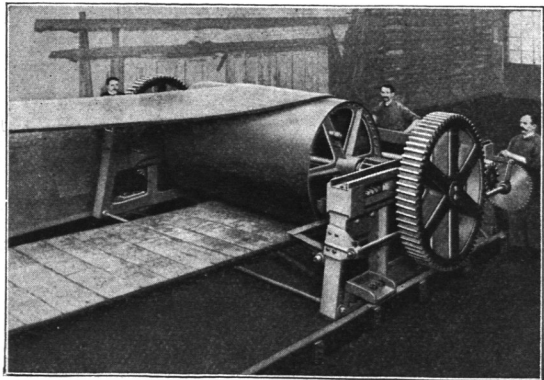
C. Otto Gehrckens, große Einlaufmaschine.
